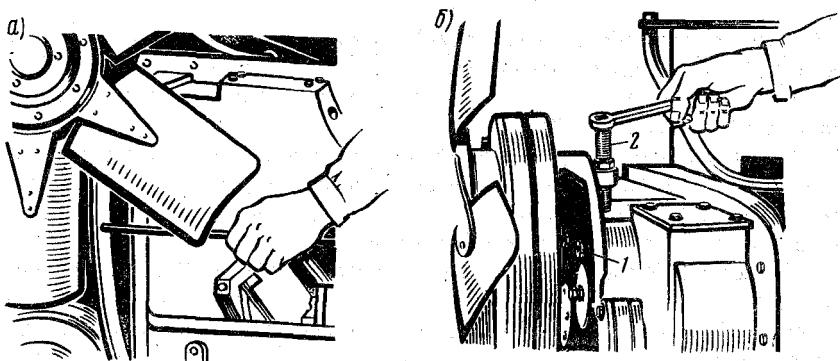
Схема регулировки натяжения ремня вентилятора двигателя Д-130М:
